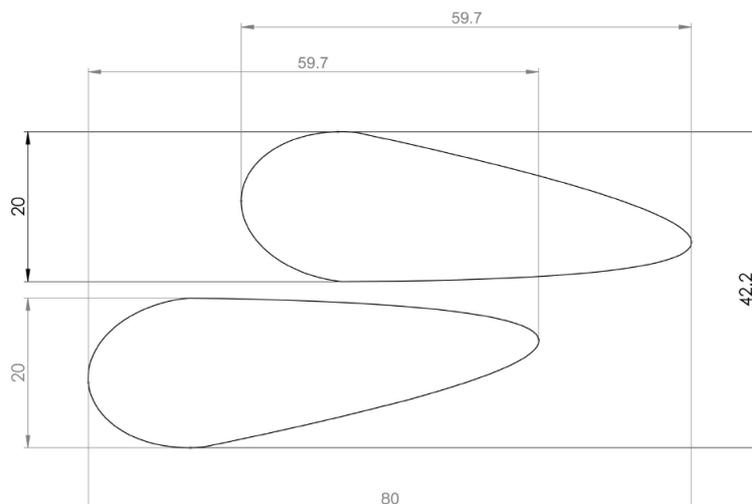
Ejemplo conforme de sección de un elemento formado por dos tubos (sección mínima de 1 cm aplicado a la horquilla, los cables y los soportes)
